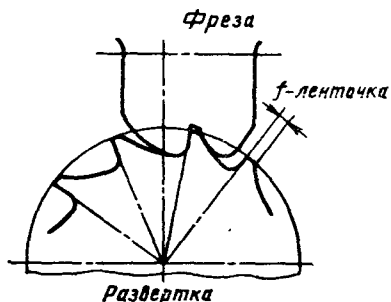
Схема работы двузубой фрезы для обработки канавок разверток
